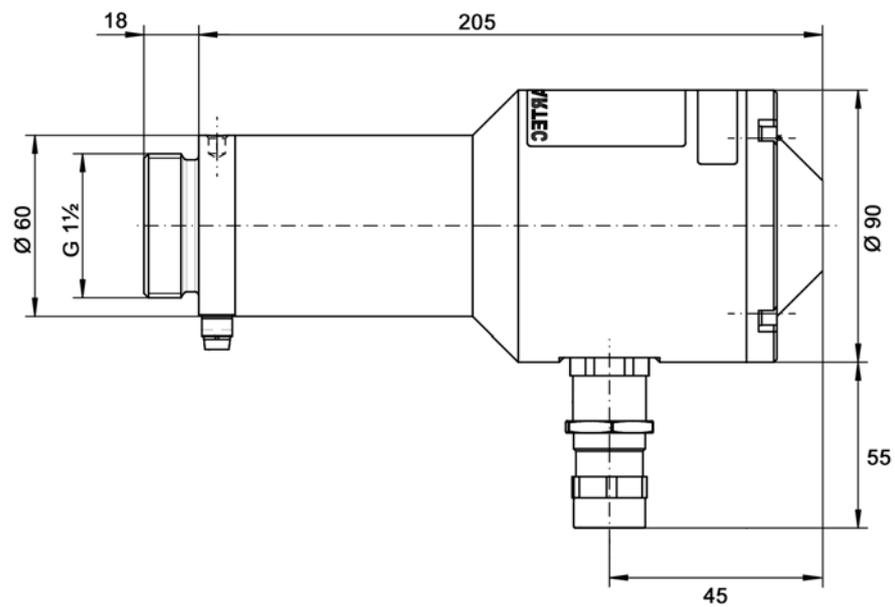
Maßzeichnung Kompaktflammwächter F200K Ex (für Ex-Zone 1, 21)
